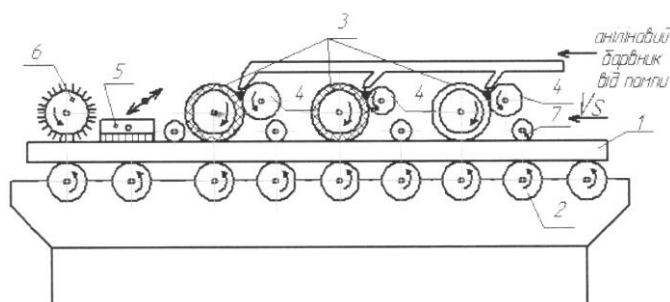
Принципова схема вальцевого верстата для фарбування деталей:
